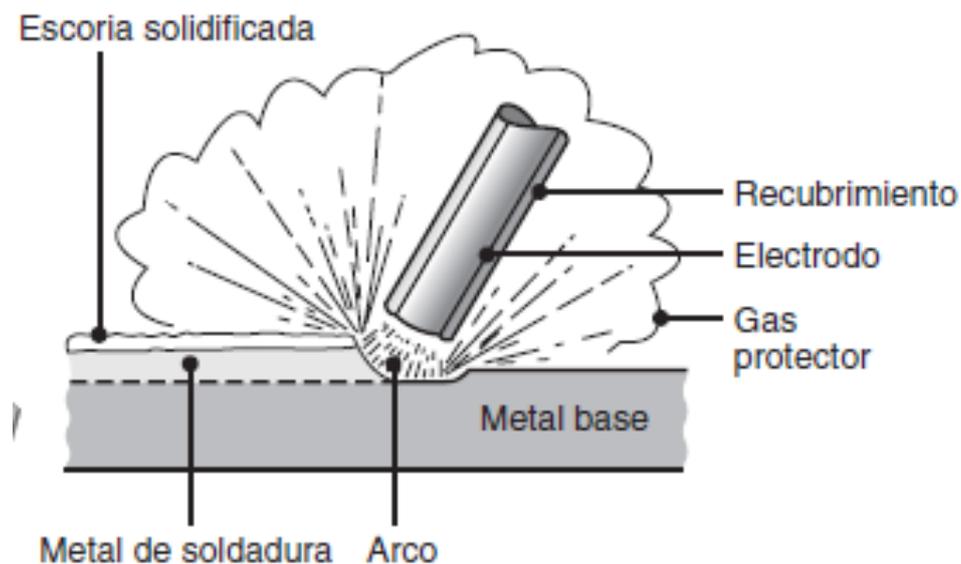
Soldadura con arco y metal protegido (Fuente: Manufactura, Ingeniería y Tecnología)
